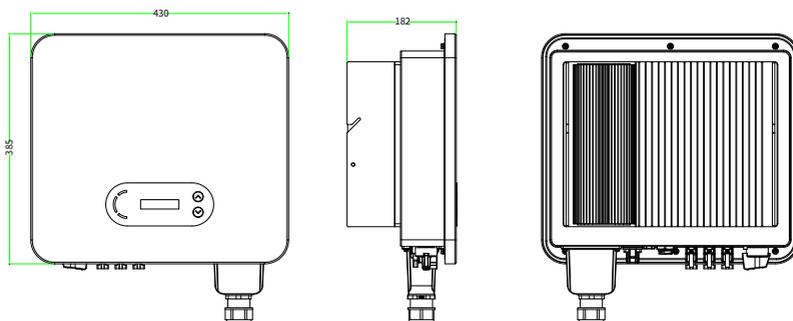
Avant, côté et arrière de la machine (3.3~12K)
